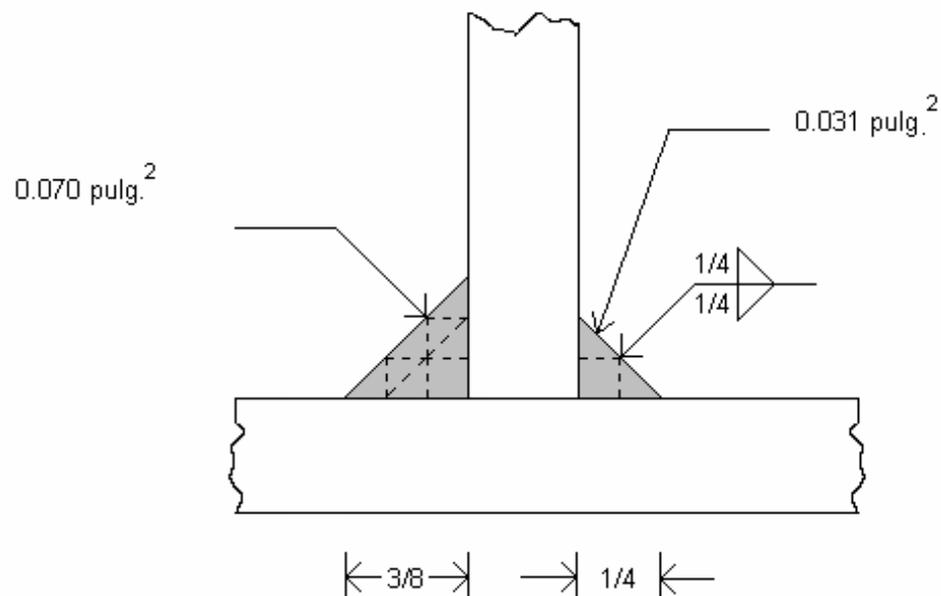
Efectos de la soldadura sobre los requerimientos de metal de aporte para una soldadura de bisel
